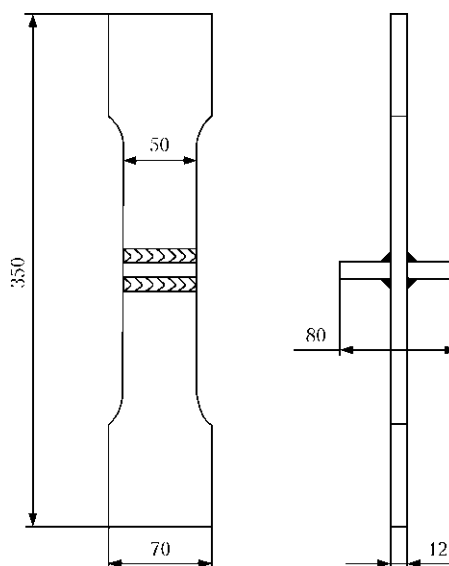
Форма и размеры образца таврового соединения стали 09Г2С
